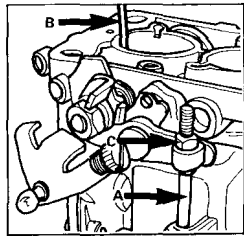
Регулировка клапана разбалансировки поплавковой камеры на карбюраторе Weber
